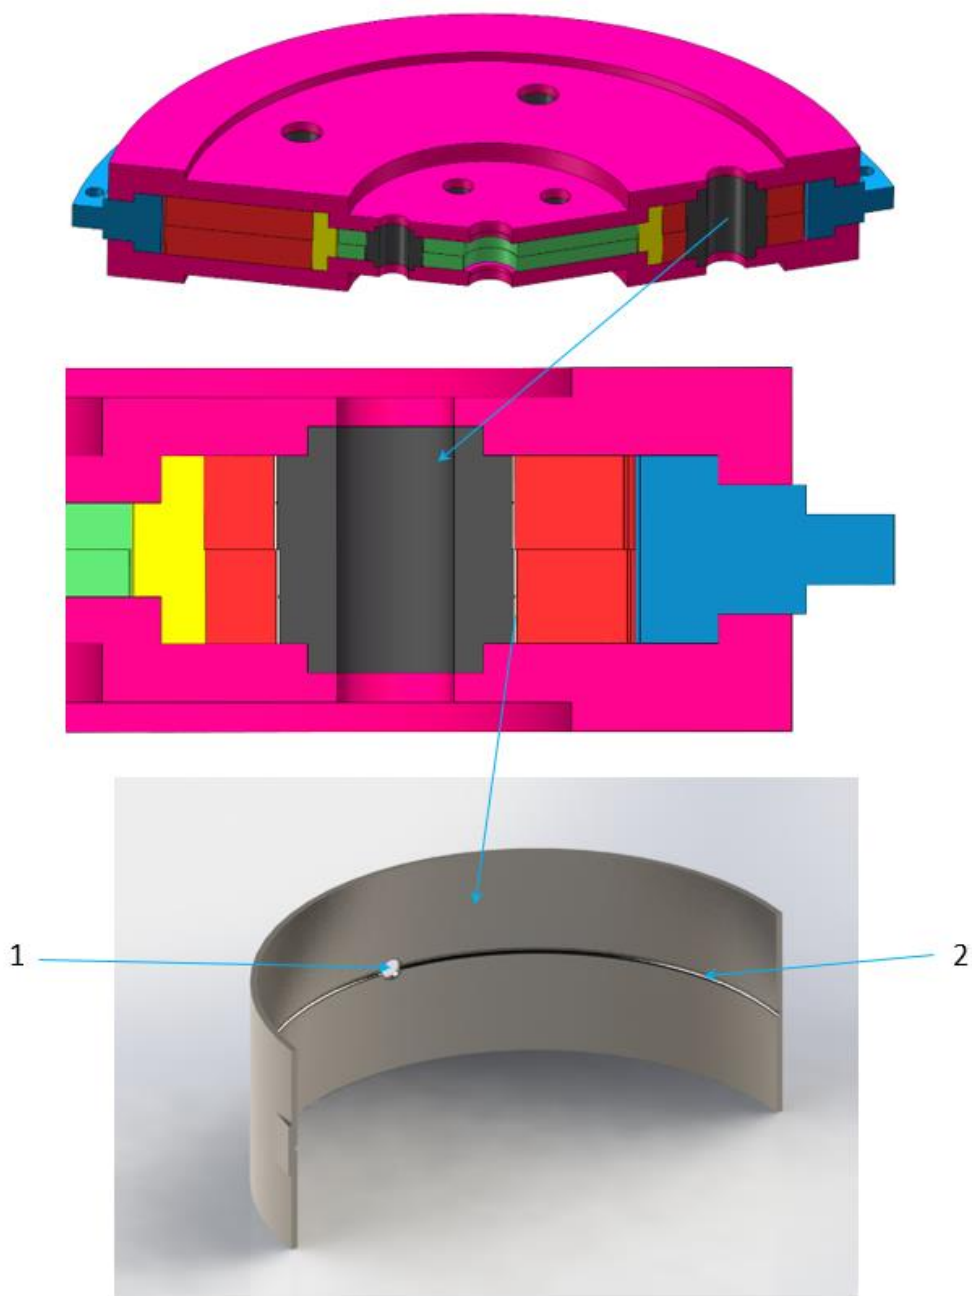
3D моделирование вида в плане и деталей редуктора и сменного подшипника.
